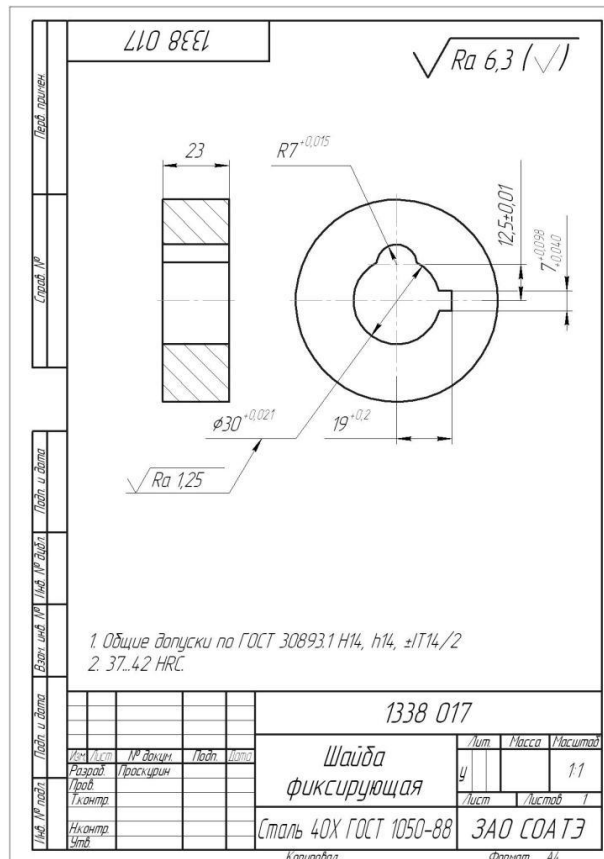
Деталь испытательного стенда. Шайба фикс
